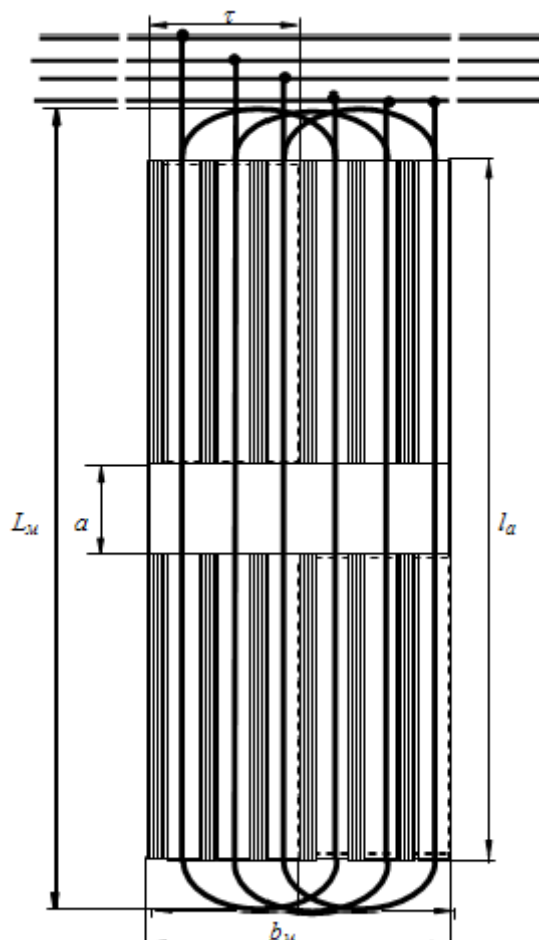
Індуктор блока-модуля ЛТЕД з три-фазною обмоткою(вид зверху)
